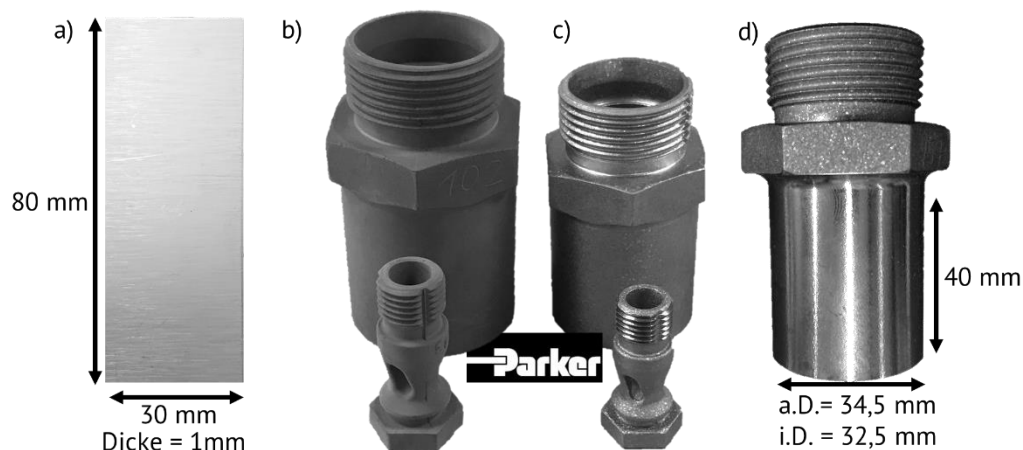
a) Ti6Al4V-Blechprobe und die Stadien eines MIM-Fittings bis zur Schweißprobe b) Grünkörper, c) gesintert mit Übermaß und d) endbearbeitetes Fitting (b und c mit freundlicher Genehmigung der Parker Hannifin GmbH)
